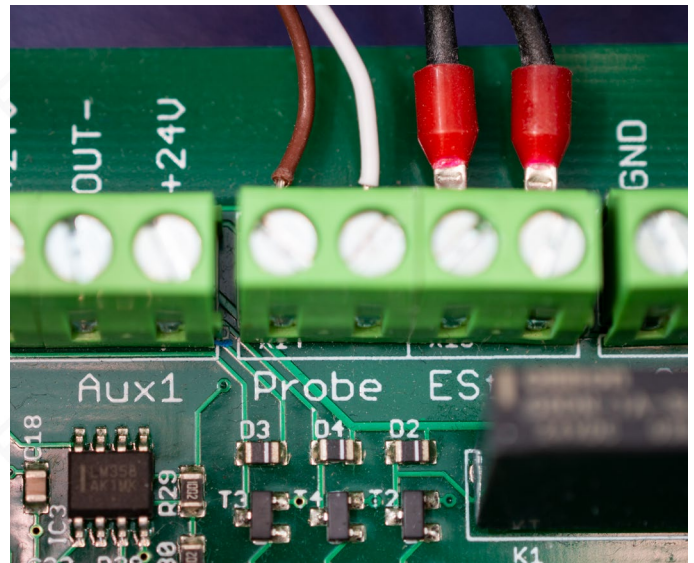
Anschluss des Werkzeuglängensensors, hier mit brauner und weißer Ader. Rechts daneben der Notaus.
